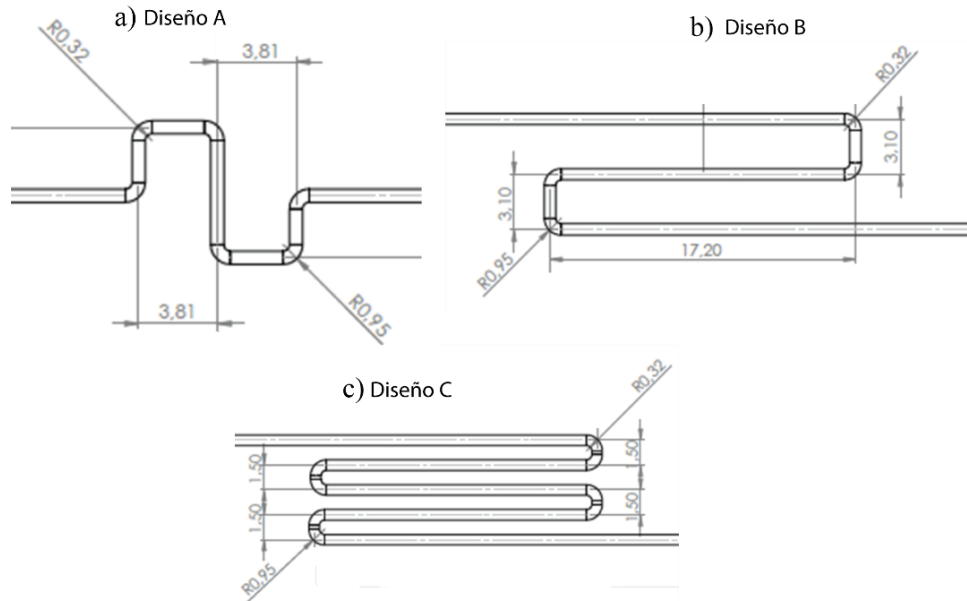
Dimensiones de las juntas: a) Diseño A, b) Diseño B, c) Diseño C. Dimensiones en [mm]
